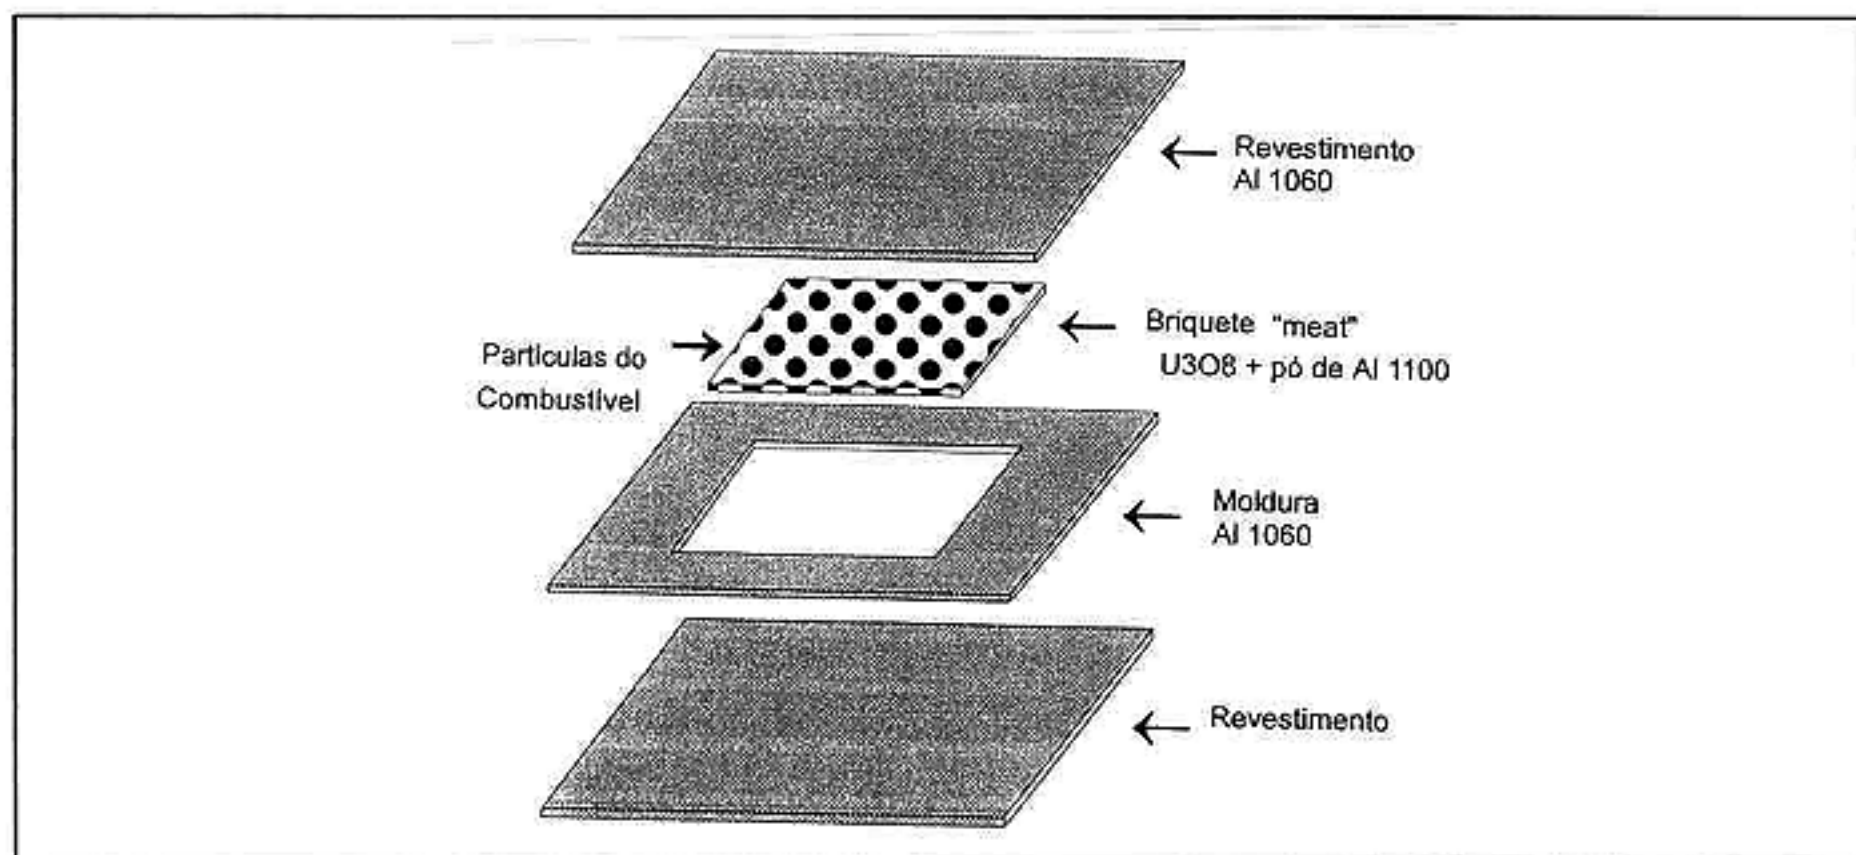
Perspectiva explodida do conjunto briquete-moldura-revestimento
